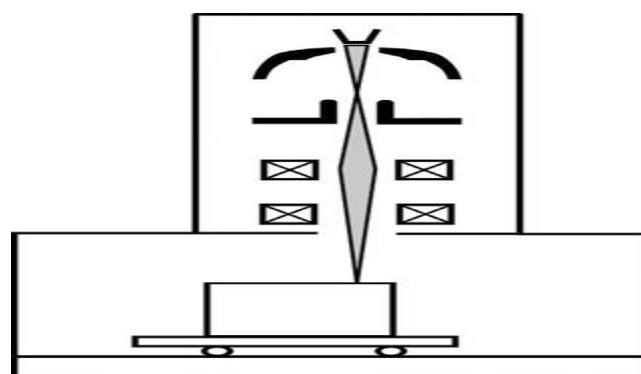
principe du soudage par faisceau d'électrons[24]
